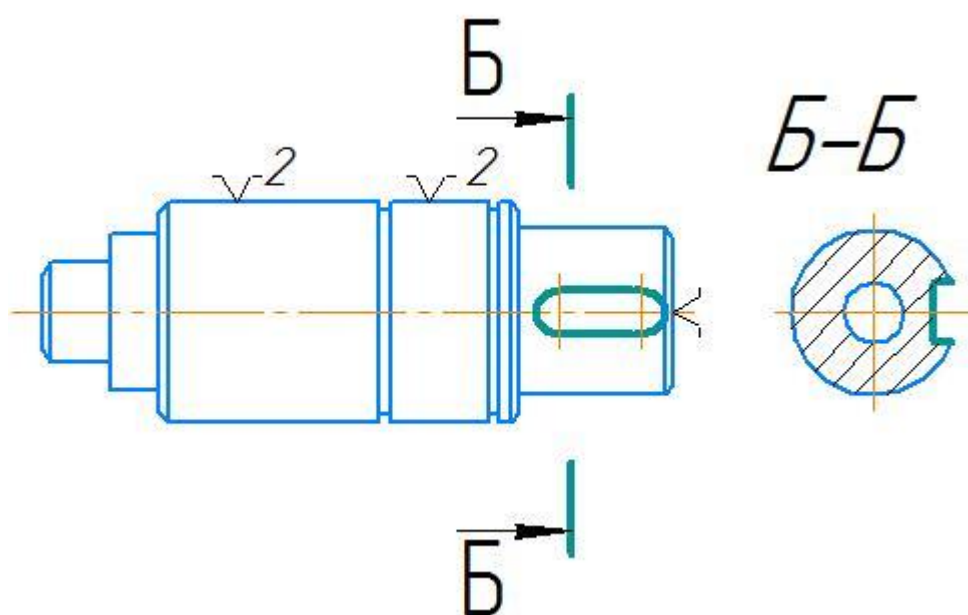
Эскиз для фрезерной операции с ЧПУ
